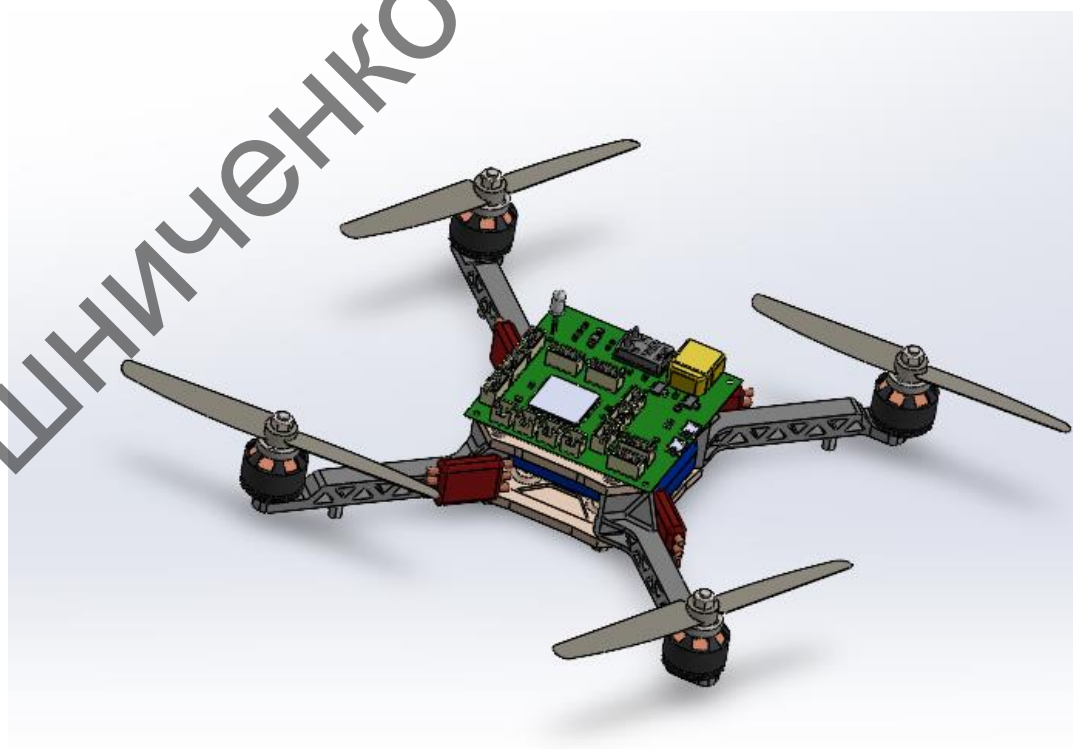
Корпус квадрокоптера в середовищі SolidWorks
